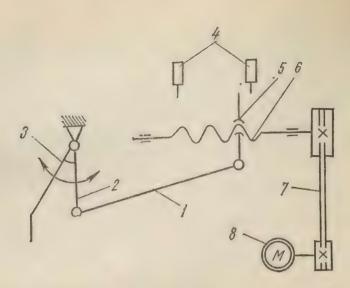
Схема привода для открытия шибера загрузочного ковша
